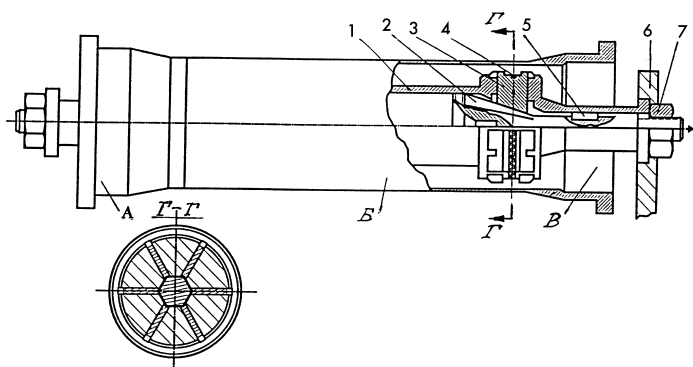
Разжимное приспособление для сборки деталей модельной емкости под сварку фланцев (А и В) с обечайкой (Б):
